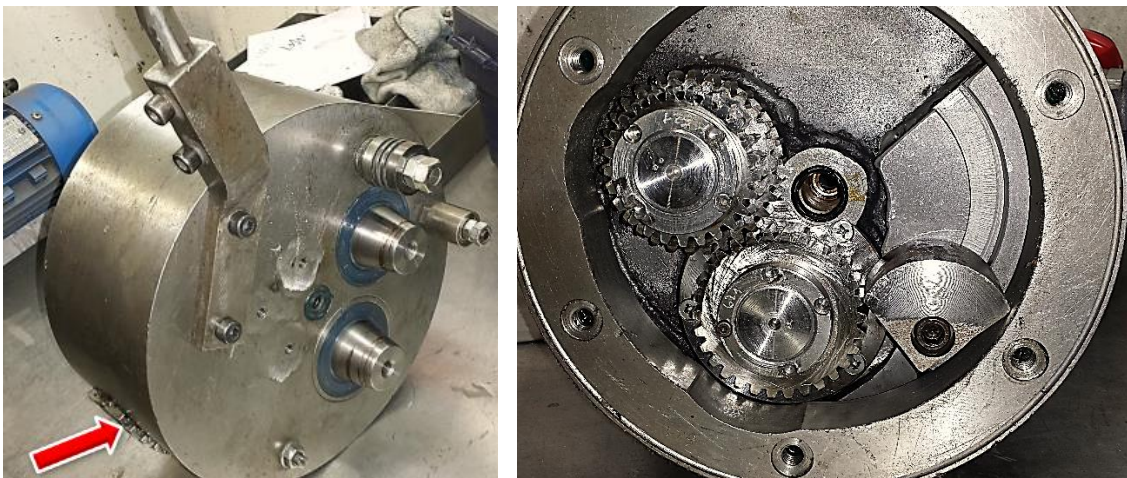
Cabeça desmontada e ilustração dos elementos internos, englobando engrenagens que transmitem o movimento aos rolos laminadores.
